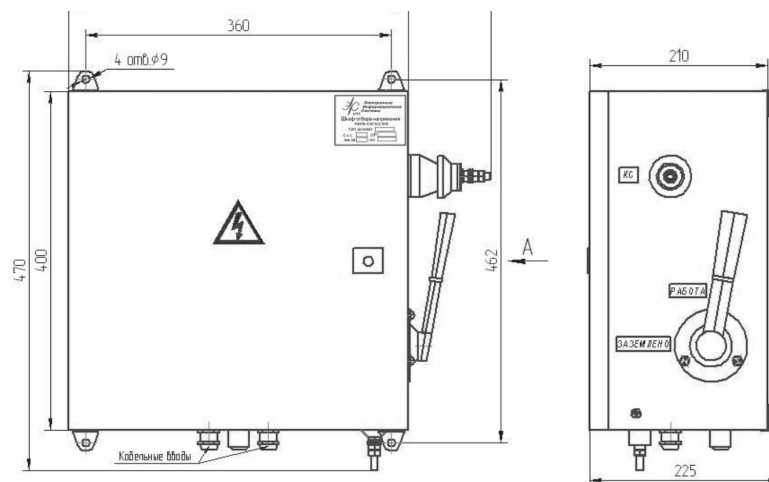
Габаритно-присоединительный чертеж Фильтр-ШОН.
